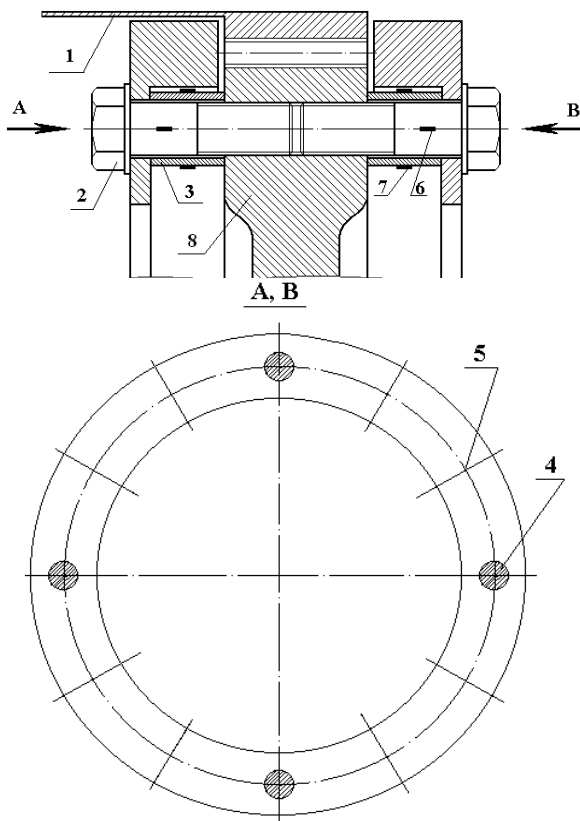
Сопряжение гибкого колеса со ступицей выходного вала редуктора: 1 – гибкое колесо; 2 – болт; 3 – упругая втулка; 4 – отверстия с тензометрическими болтами и втулками; 5 – свободные отверстия; 6, 7 – тензорезисторы; 8 – ступица выходного вала
